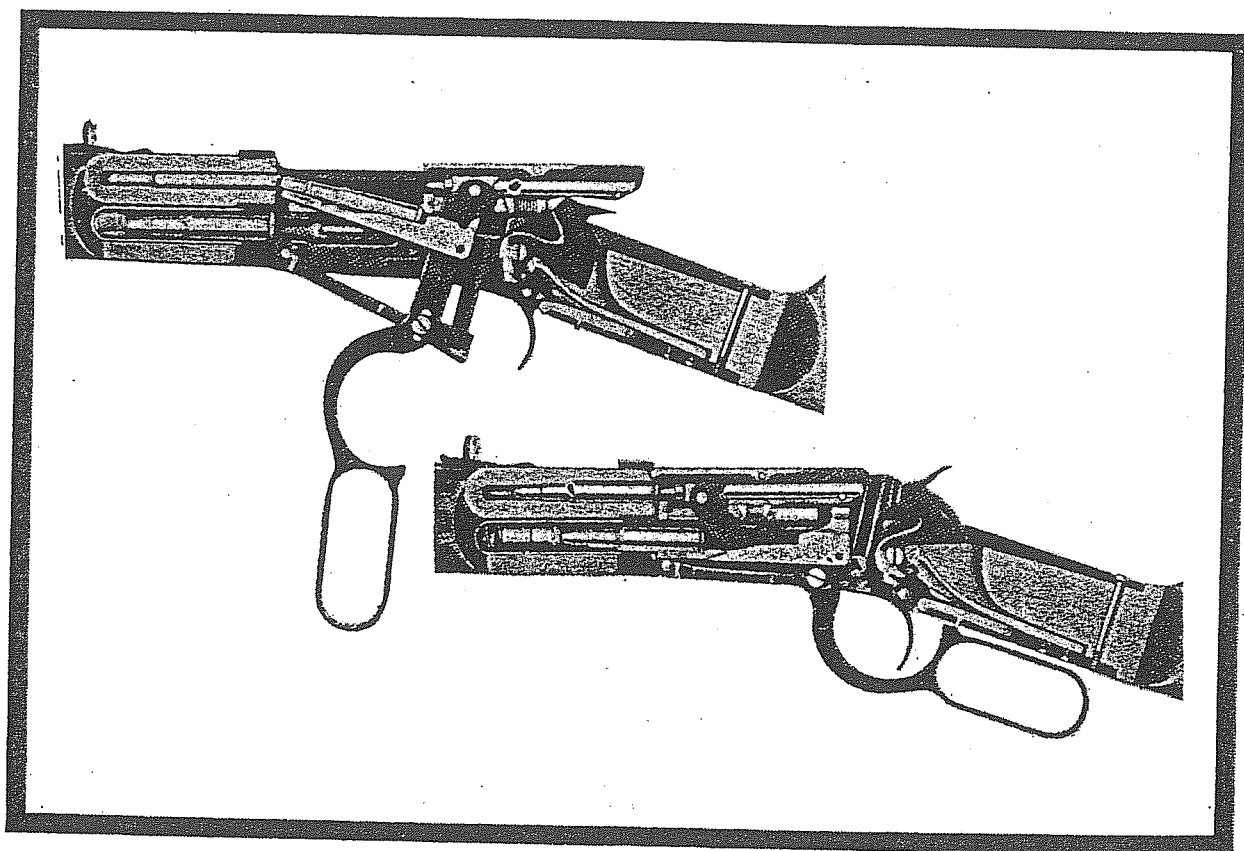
Meccanismo del mod. 94 Winchester a leva (aperto e chiuso).
